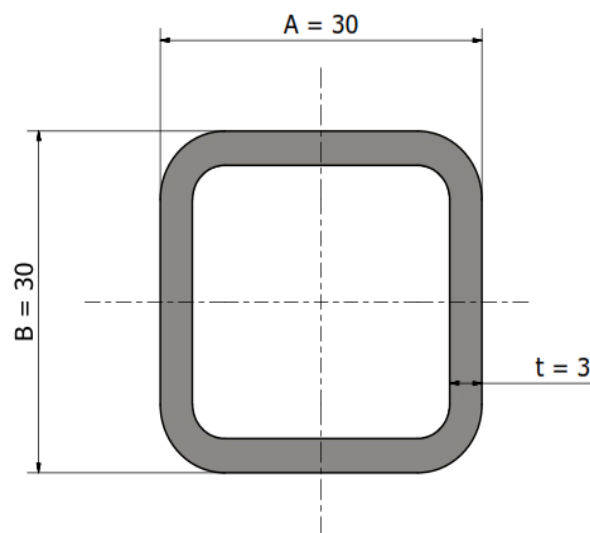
Dimensiones en mm del perfil cuadrado.
